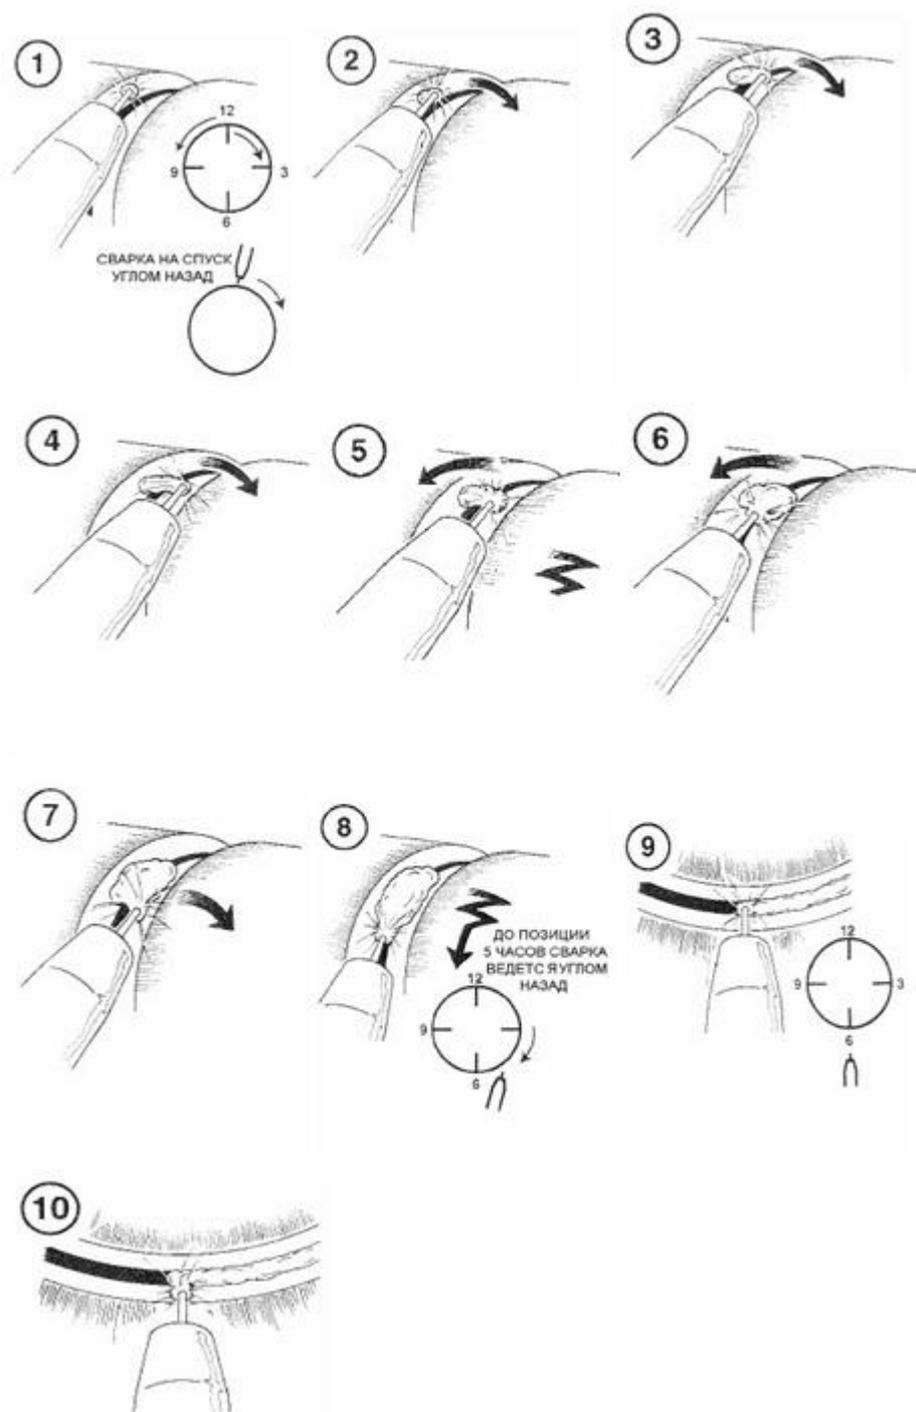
Процесс изготовления стыкового сварного соединения при помощи STT процесса
